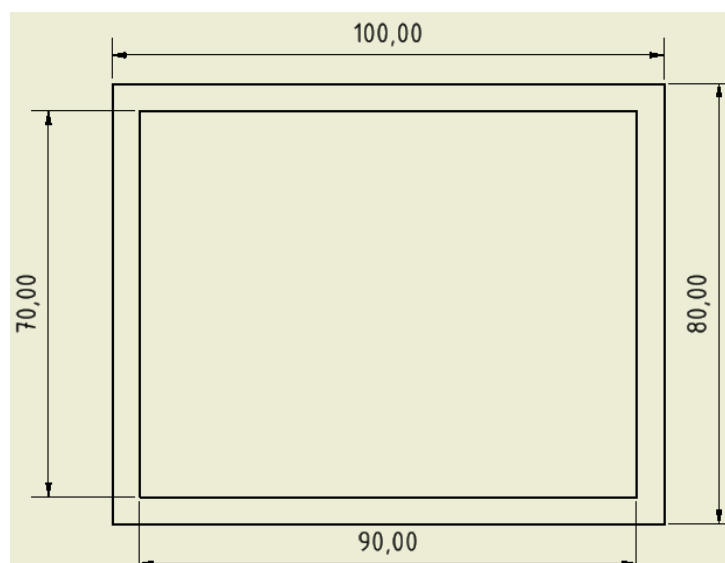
Planos caja Arduino parte dos. (Fuente los autores).
